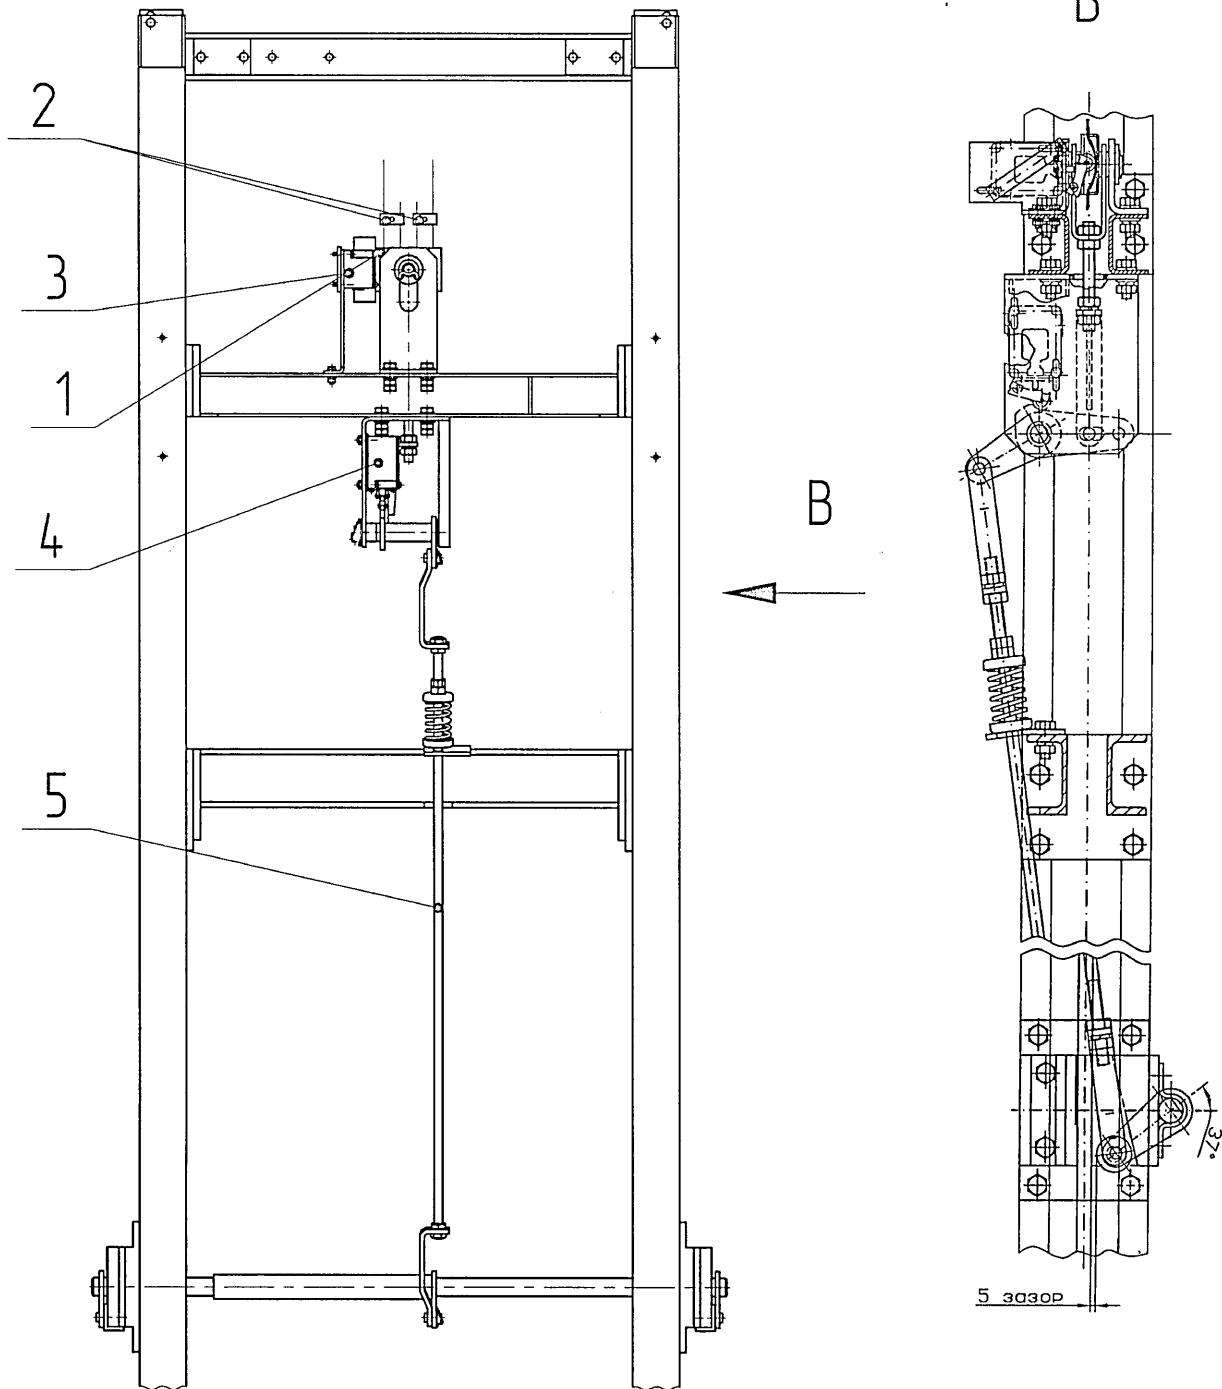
установка шунтов, датчиков и конечного выключателя
